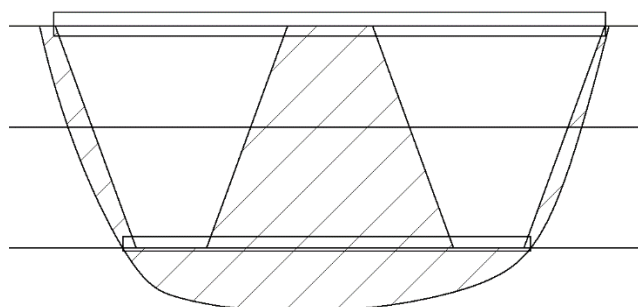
3-й місцевий розріз, деталь – оболонка циліндричного черв'яка
